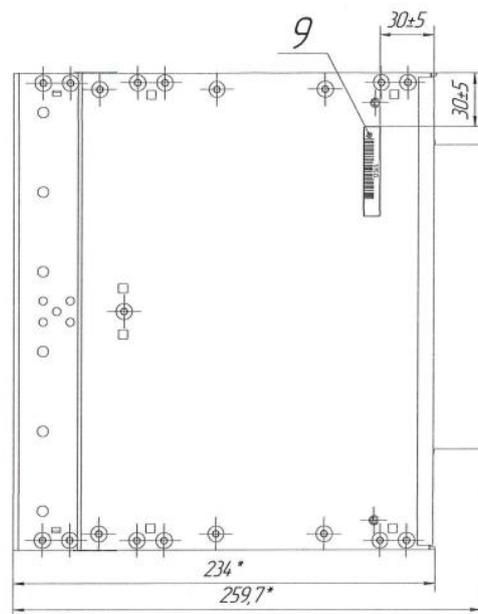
Габаритные и установочные размеры ЭКРА 253 01XX (вид сбоку)
